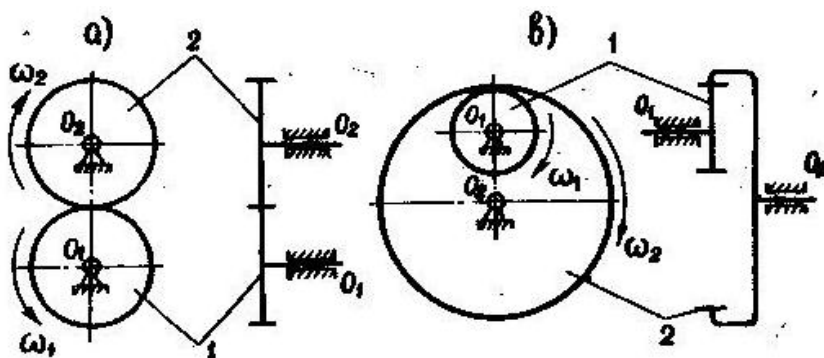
Схемы, зацеплений зубчатых колес:
